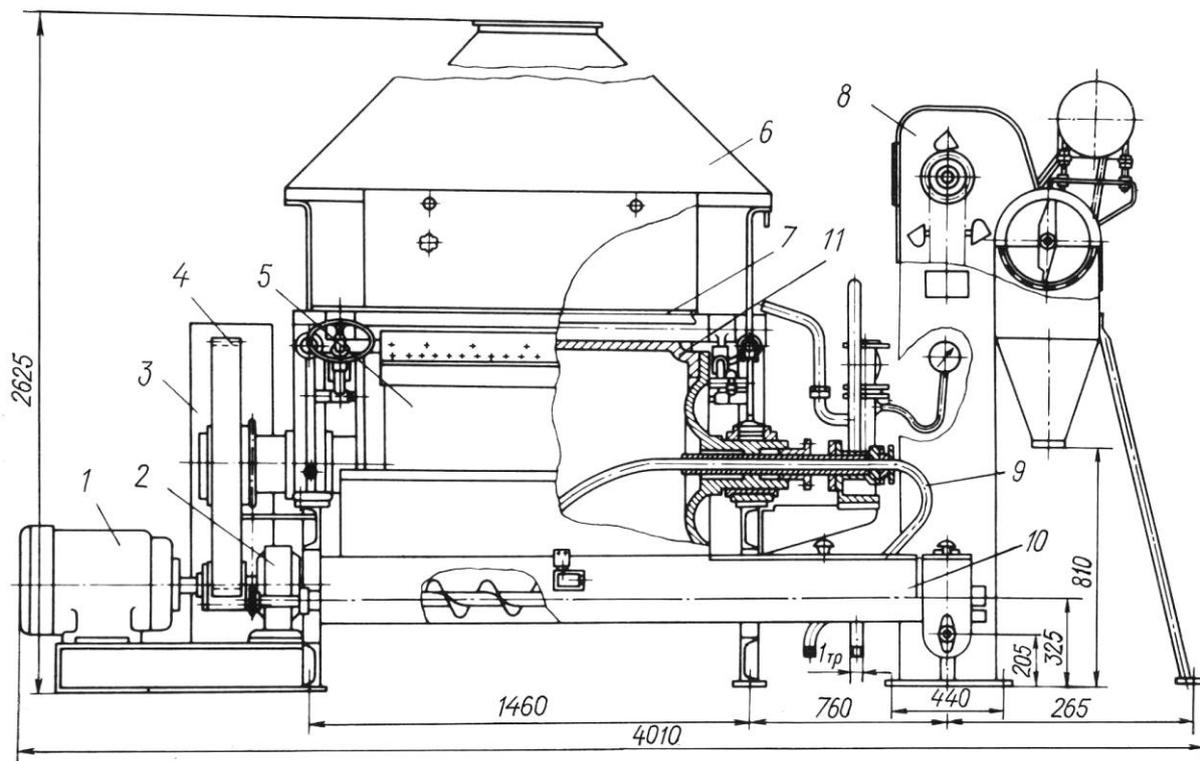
Сушильно-дробильный агрегат марки СДА-250: 1 – двигатель; 2 – редуктор; 3 – ограждение; 4 – открытая зубчатая передача; 5 – сушилка; 6 – системы вытяжки; 7 – коллектор; 8 – дробилка; 9 – трубопровод; 10 – шнеки; 11 – валец
